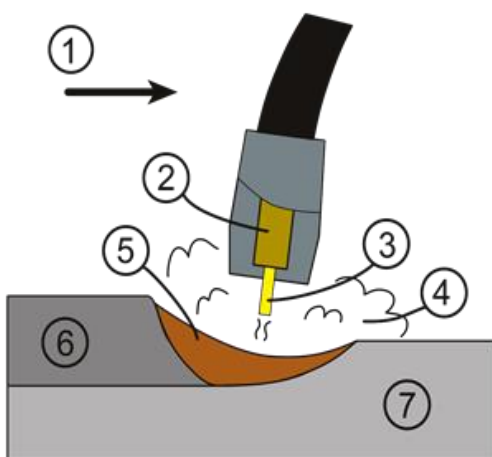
Skema Gas Tungsena Arc-welding
